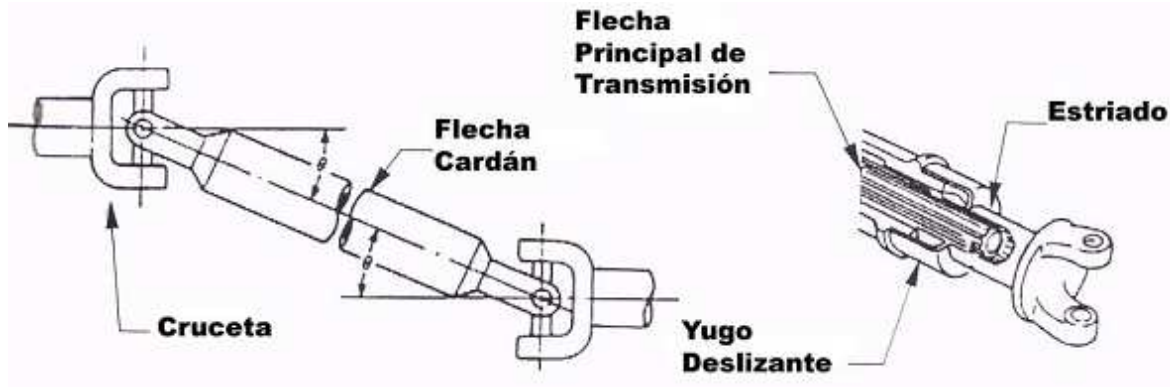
Junta universal, Flecha cardán y yugo deslizable
